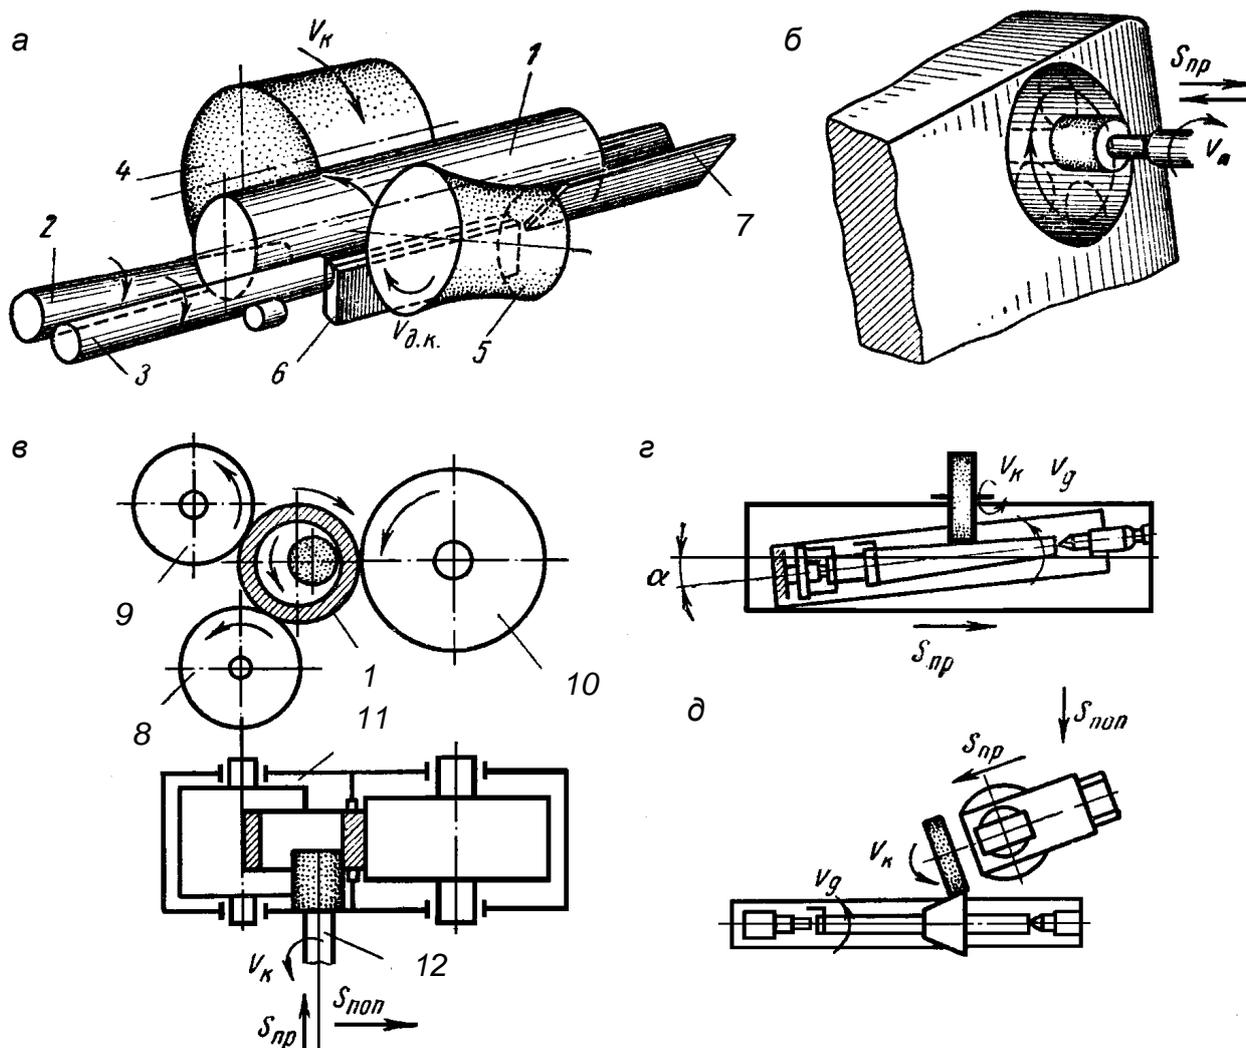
Основные виды шлифования наружных, внутренних и конических поверхностей: а – шлифование цилиндрической поверхности; б – обработка внутреннего цилиндрического отверстия; в – шлифование отверстий колец; г, д – шлифование наружных конических поверхностей; 1 – деталь; 2, 3 – загрузочные валики; 4 – шлифующий круг; 5 – ведущий круг; 6 – упор; 7 – направляющие планки; 8 – поддерживающий ролик; 9 – прижимной ролик; 10 – ведущий ролик; 11 – корпус; 12 – шпиндель
